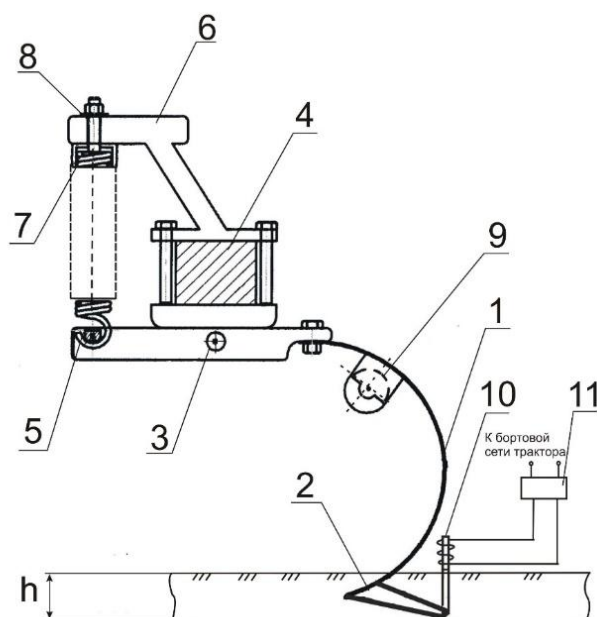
Рабочий орган культиватора (Патент РФ № 216870):
